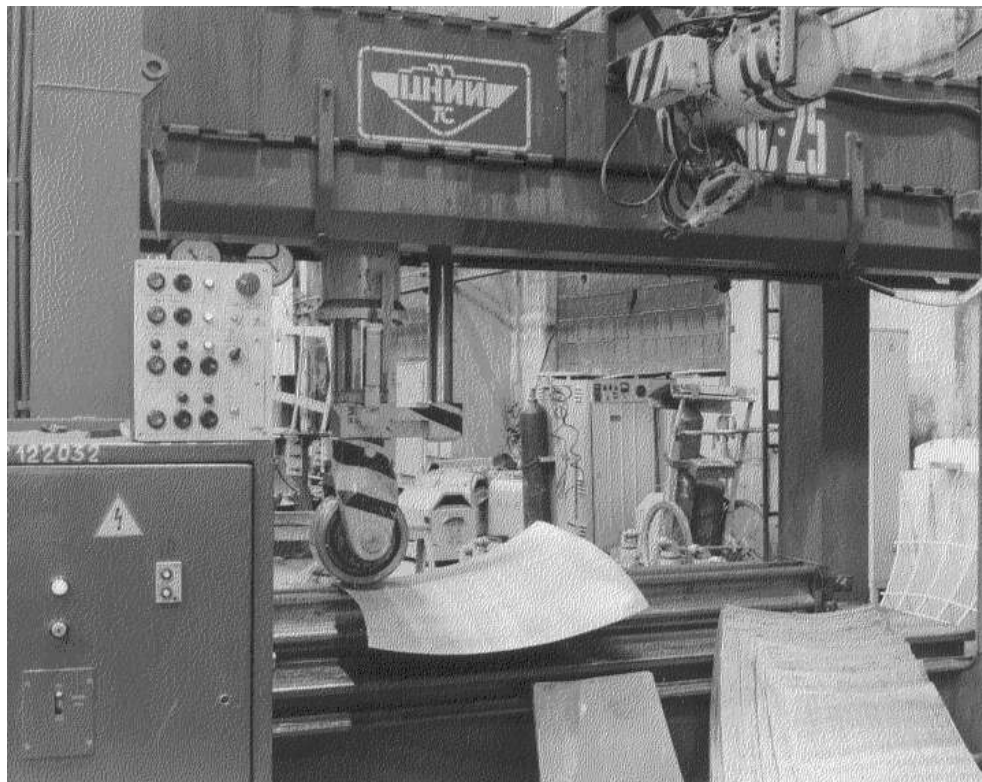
Гибка листовых деталей обшивки диффузора на станке МГПС-25
